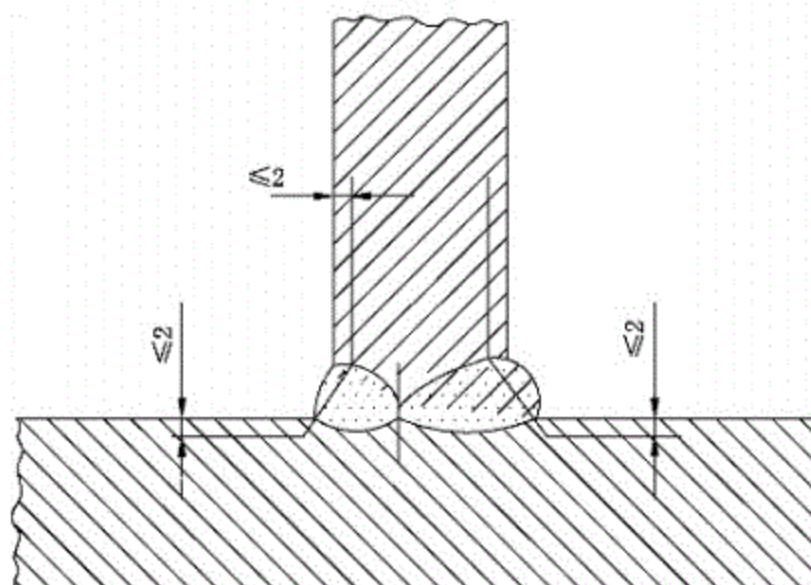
焊接接头焊缝硬度试样标线测定(R)示例
